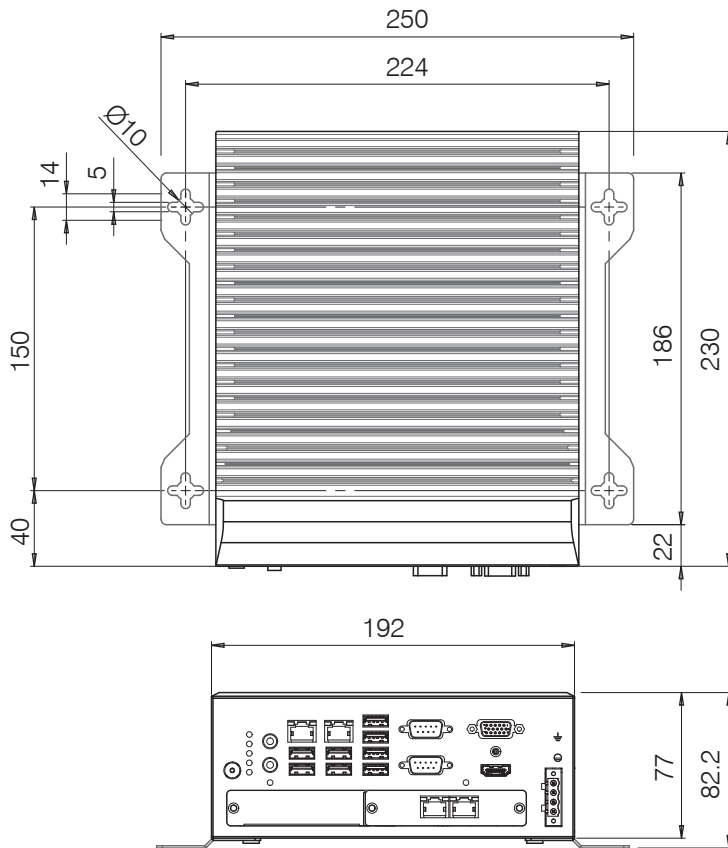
Maßzeichnung Controller SC2500 mit Montageadapter
